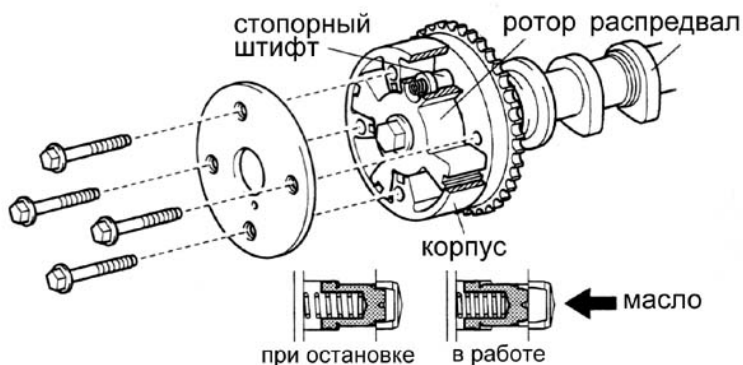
Исполнительный механизм системы VVT-i (Toyota)
